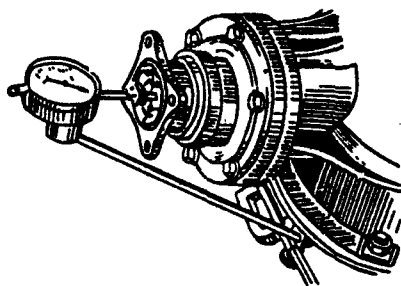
Определение осевого люфта в подшипниках вала ведущей шестерни
